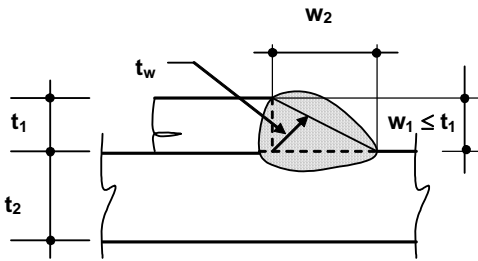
Soldadura de filete. Junta traslapada
